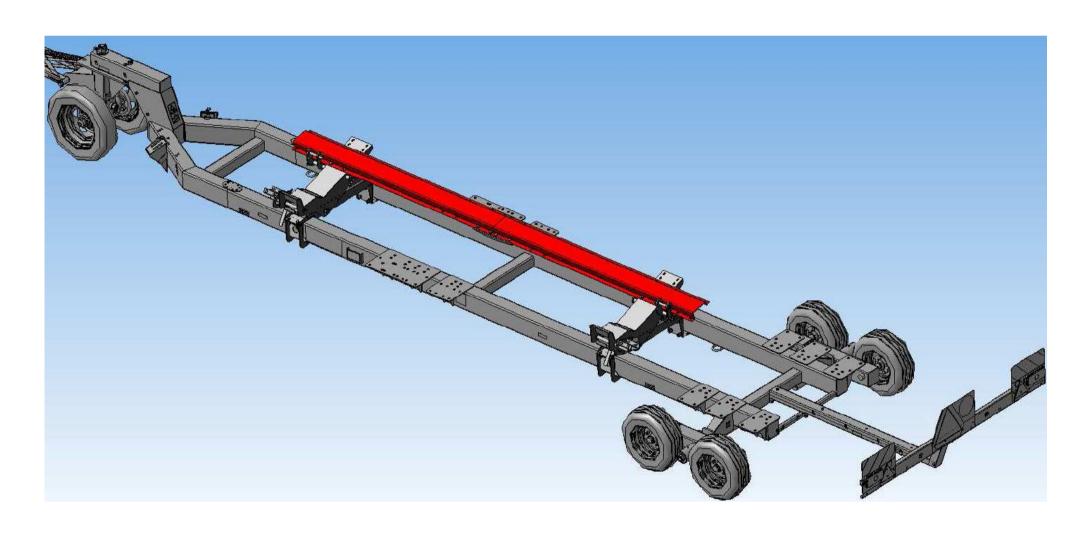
Приспособление для перемещения адаптеров ППА-4000 "Uni Cart 4000" для RSM SS-490 (с комплектом для транспортировки SS-490.13.00.000A)
